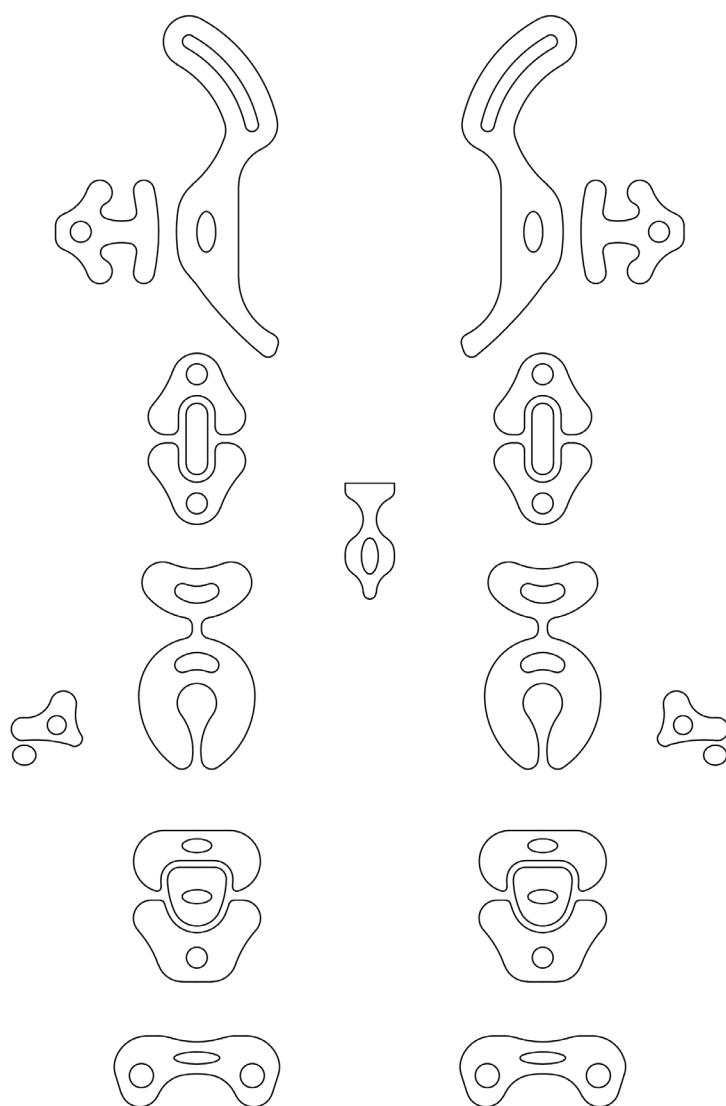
Desenhos finais das geometrias para os pads de proteção.
